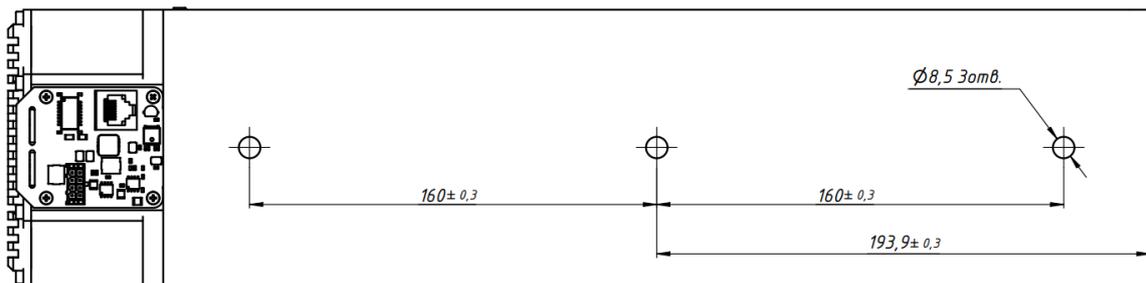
Присоединительные размеры бортового наклонного устройства
